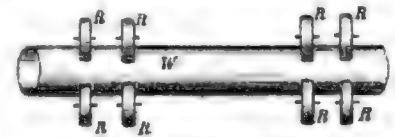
Grundriss der Welle mit den Rollen.
